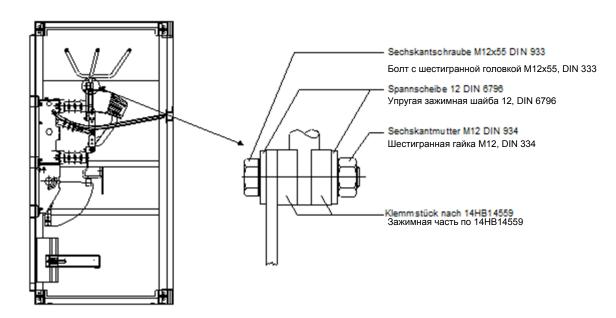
Sammelschienenanschluss Rundleiter Рис. 23-1: подключение сборной шины провода круглого сечения
